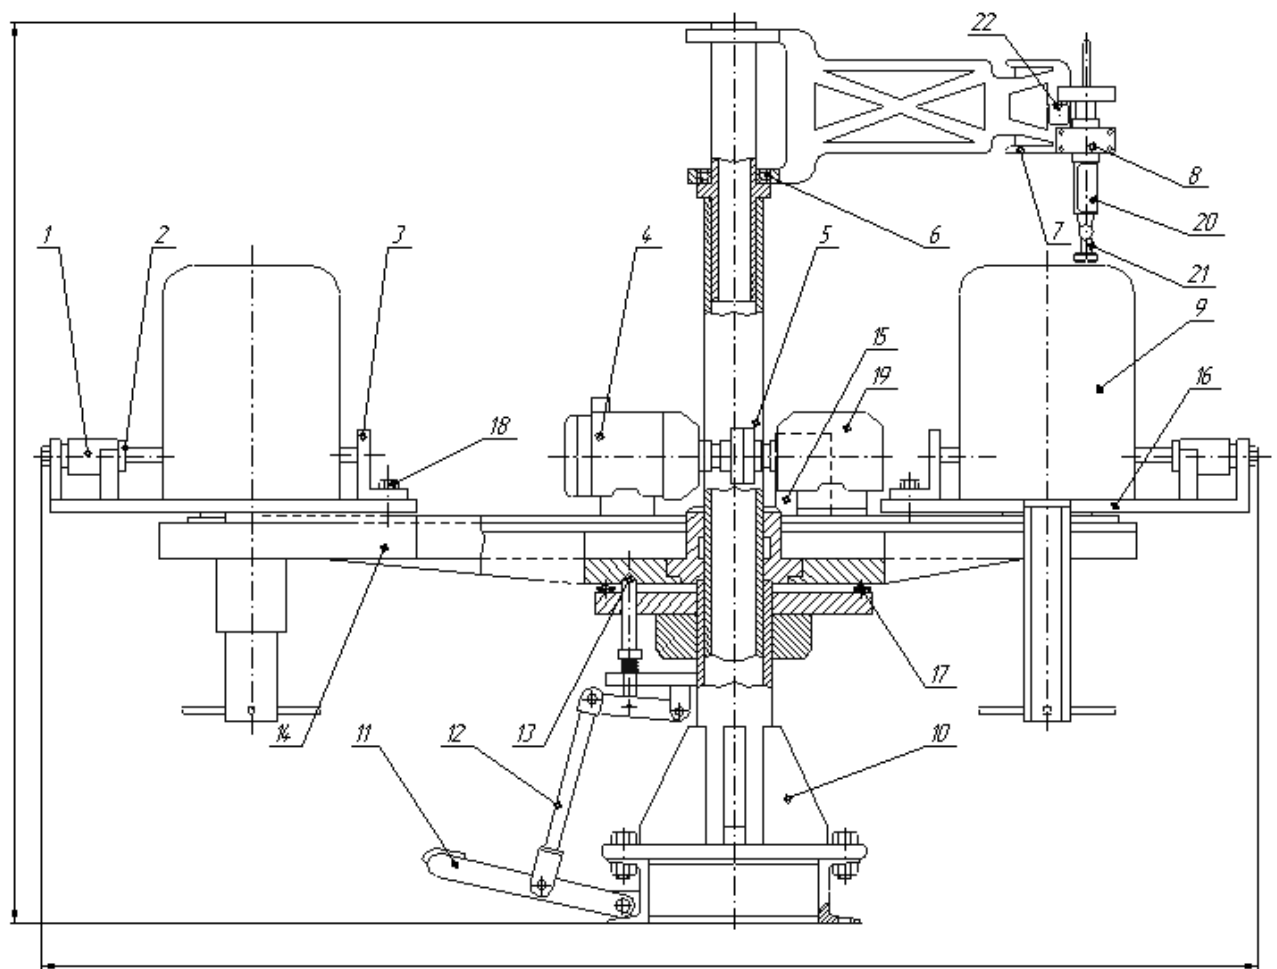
Загальний вигляд станда для ремонту коробок передач:
